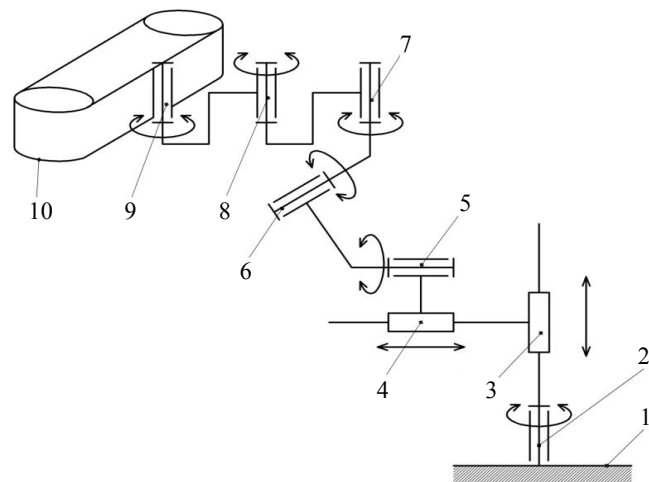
Кинематическая схема мобильного станкоробота для шлифования поверхностей катания бандажей вращающихся агрегатов
